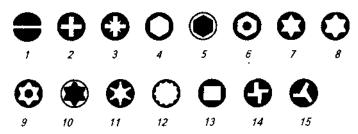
Виды рабочих профилей в головках крепежа:
